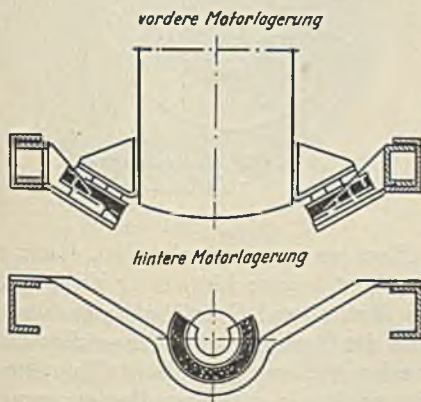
\*\*. Aufhängung für 4-Zyl.-Dieselmotore
